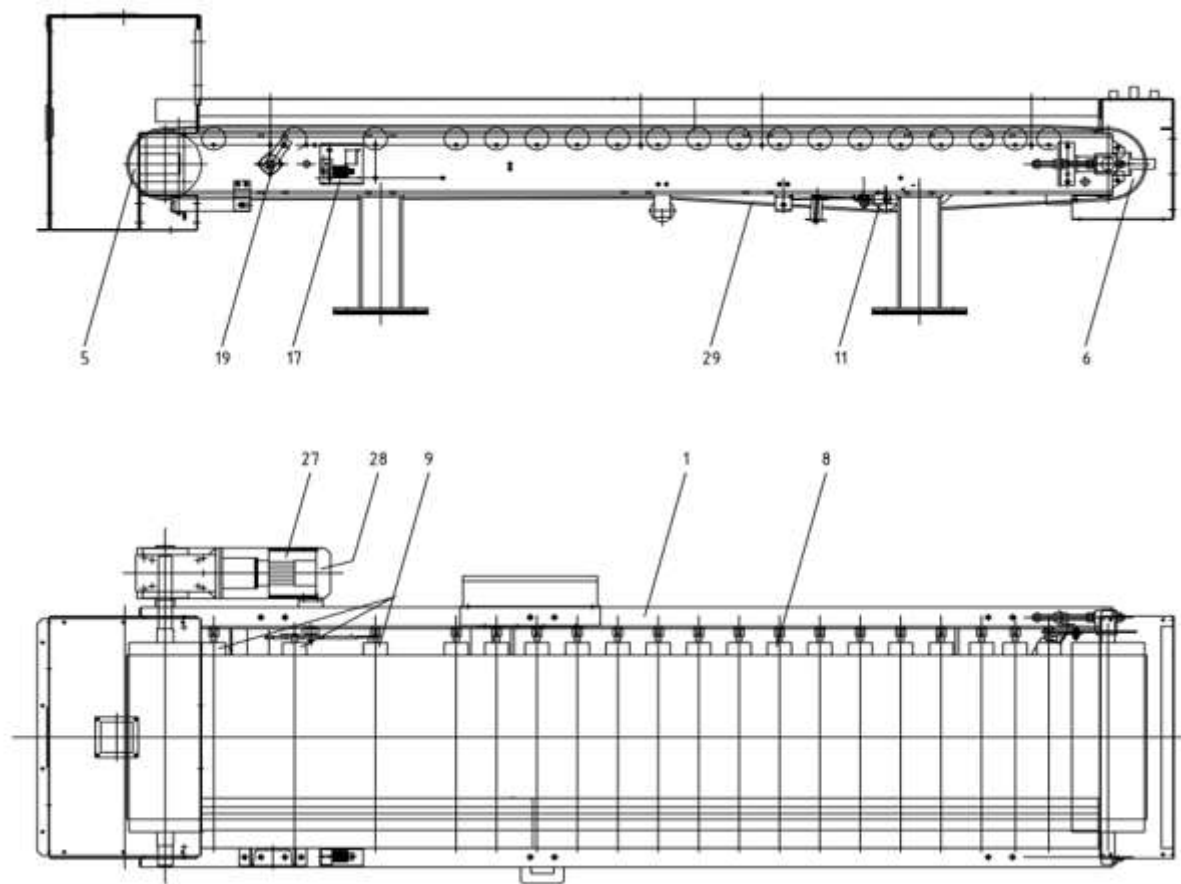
Конструкція стрічкового вагового дозатора
